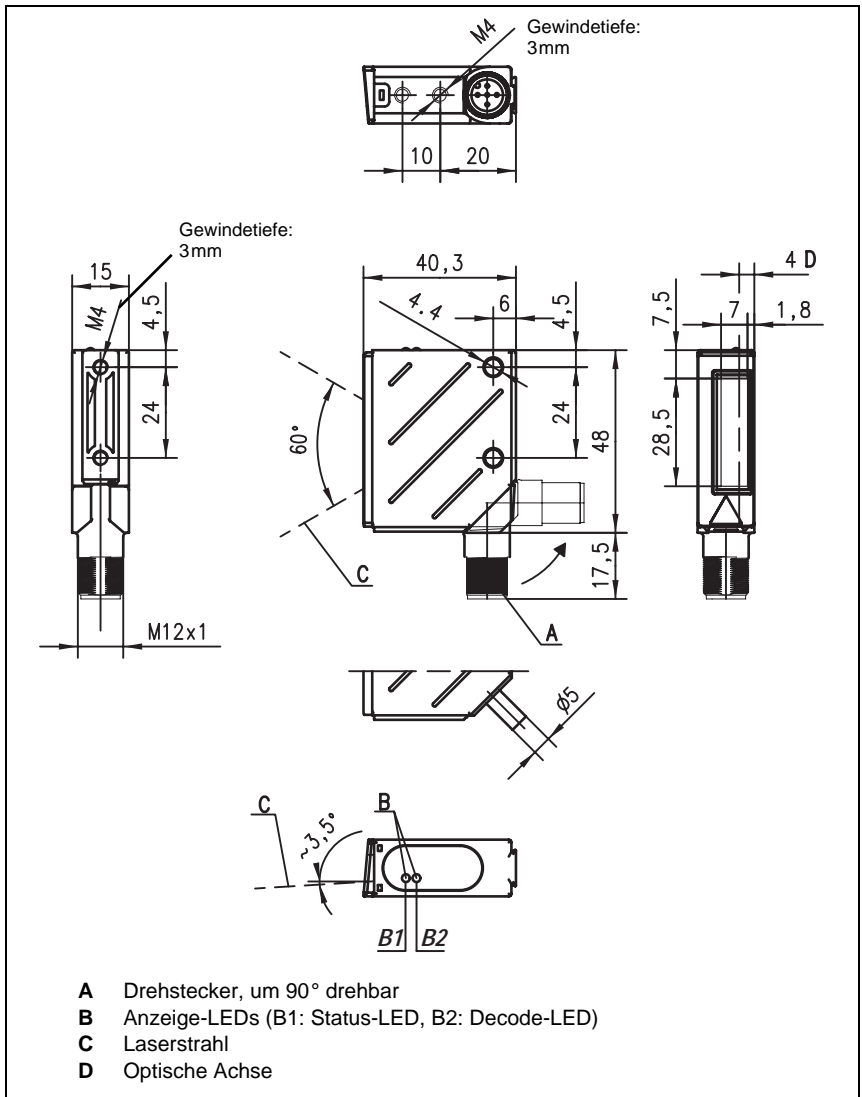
Maßzeichnung BCL 8 S M ...2 mit frontseitigem Strahlaustritt
